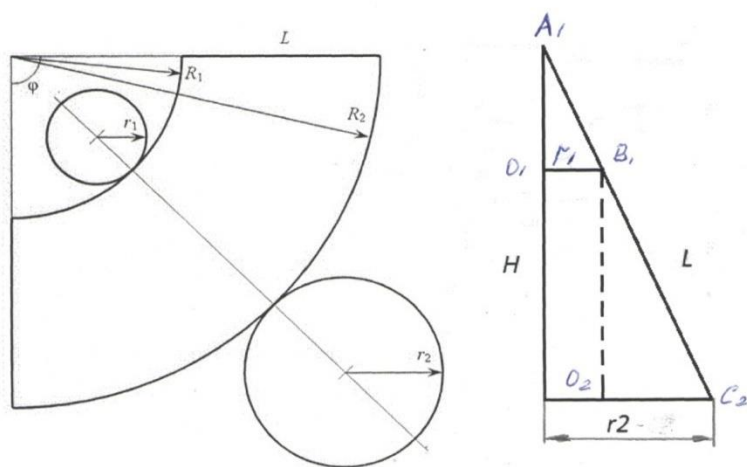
Развертка для изготовления конусных частей рассекателя
